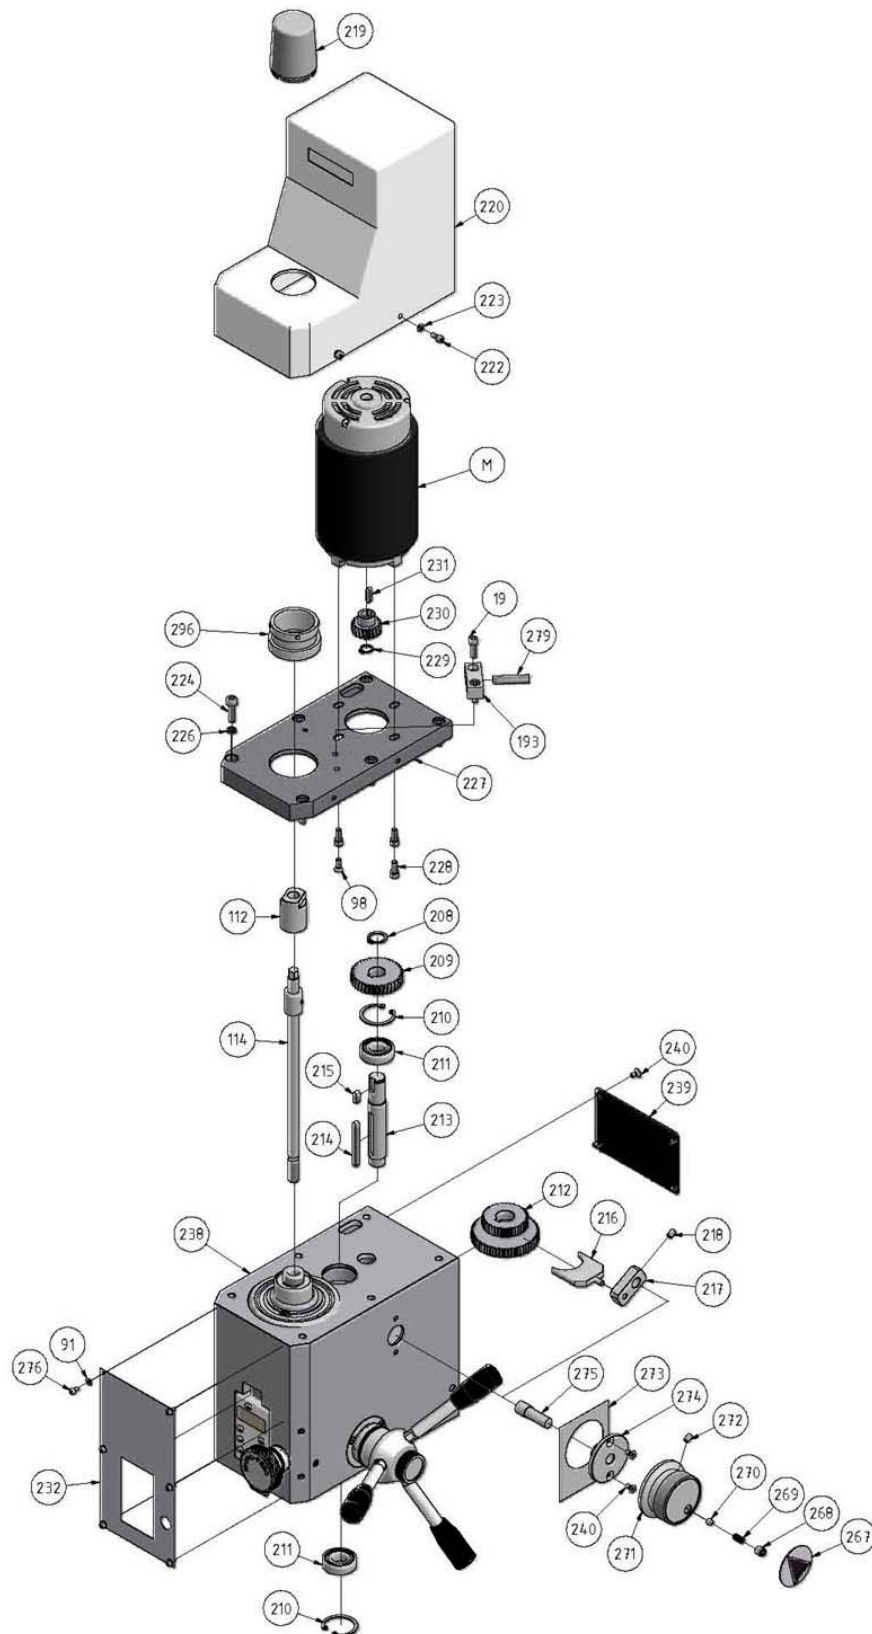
Fräskopf 1 von 2 - Milling head 1 of 2
